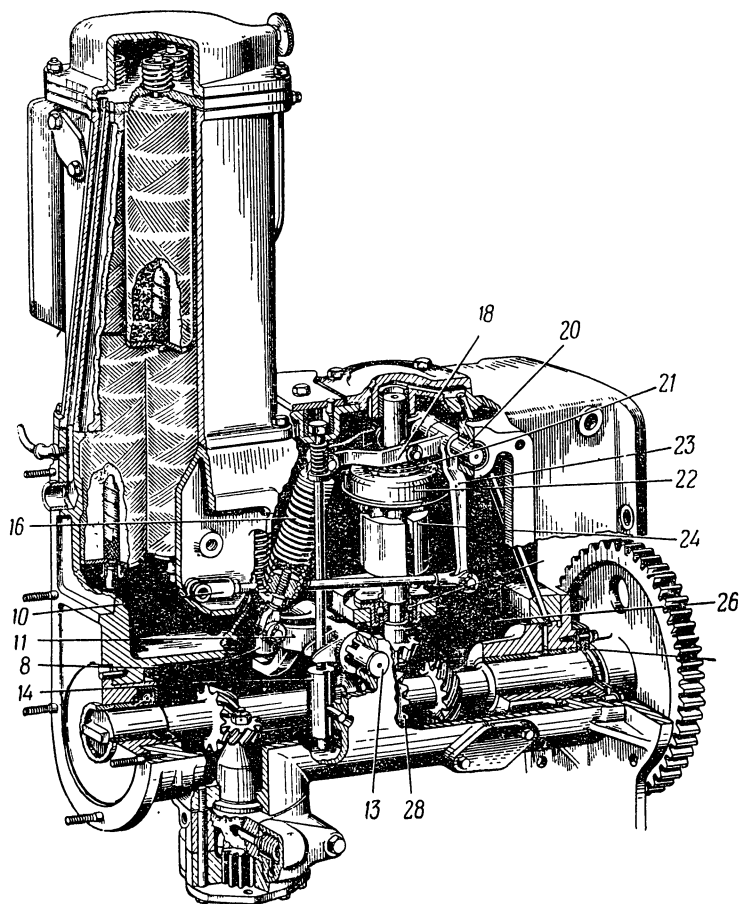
Общий вид и установка всережимного регулятора дизеля КДМ-46 (детали обозначены теми же номерами, что и на рис. 65)
